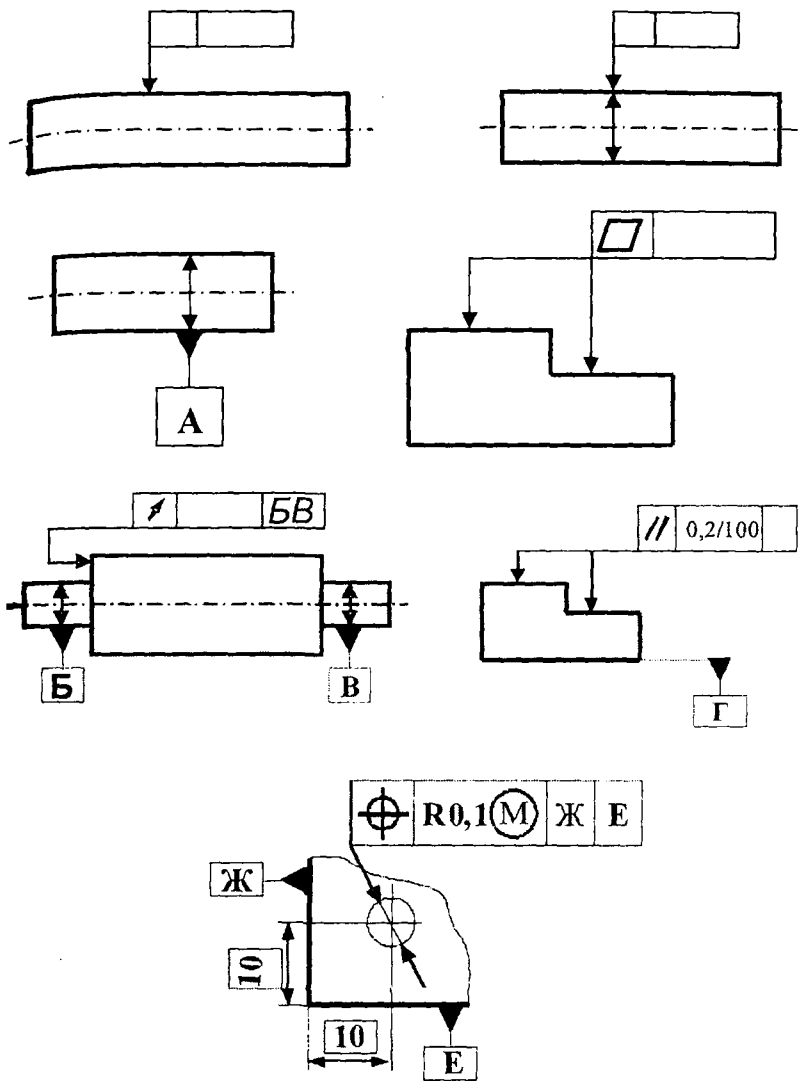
Примеры обозначений допусков формы и расположения поверхностей
